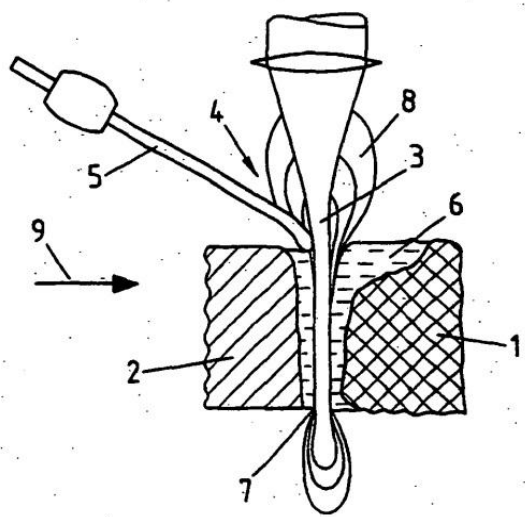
Схема ЭЛС с присадочной проволокой: 1 – сварной шов; 2 – зона соединения; 3 – луч; 4 – зона процесса; 5 – присадочная проволока; 6 – зона плавления; 7 – полость; 8 – плазма, 9 – направление движения деталей.
